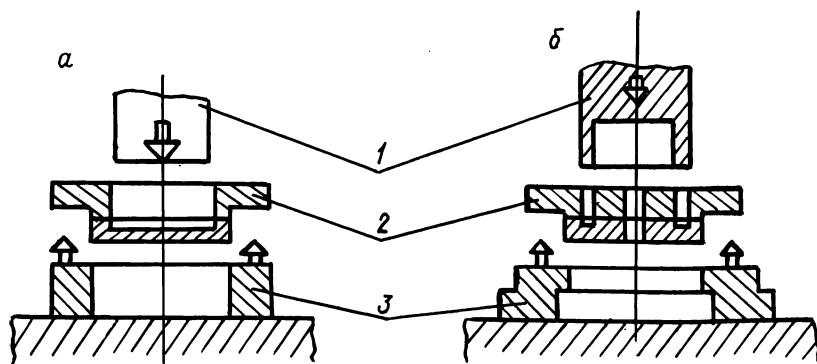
Схемы испытаний для определения прочности соединения слоев биметалла: 1 - пуансон; 2 - испытуемый образец; 3 - опорный элемент.
